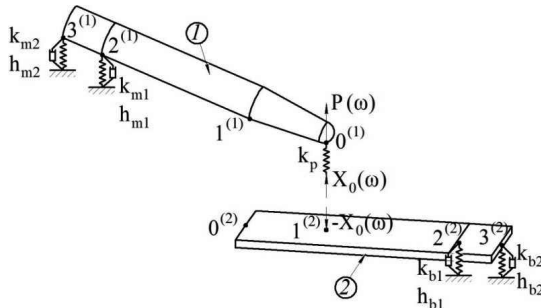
Динамічна модель кінцевого фрезерування консольно-закріпленої тонкої пластини: 1 – підсистема інструменту (кінцева фреза); 2 – підсистема заготовки (пластина)
